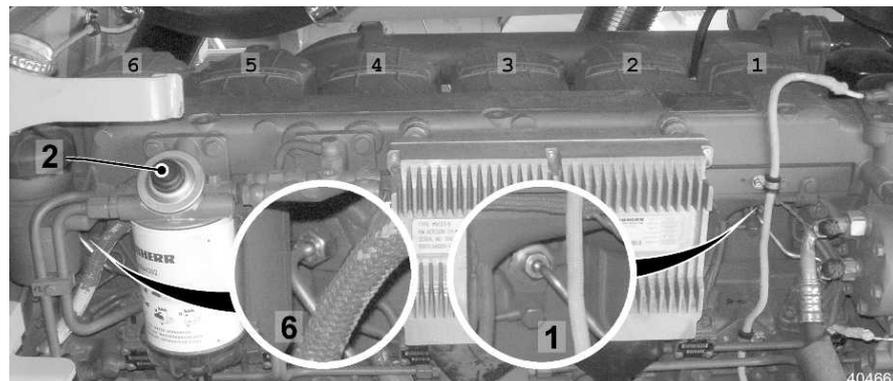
Einspritzleitungen der Zylinder 1 und 6
